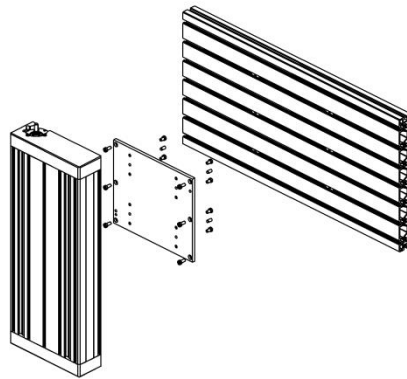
Handlingsystem iLE 20/20 für die Schlittenplattenbefestigung - Gestell
